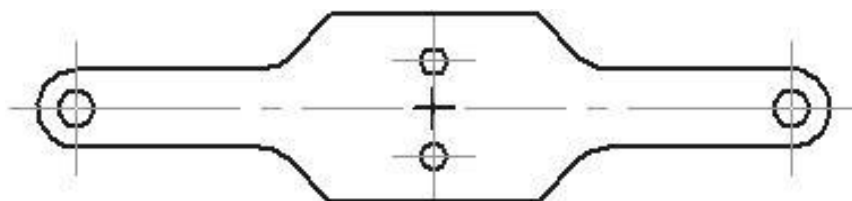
Расположение центра давления штампа детали «пластина».
